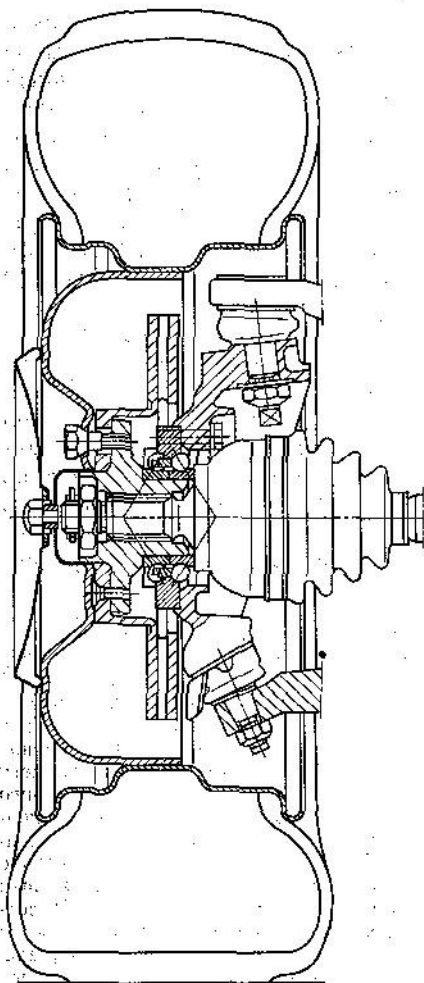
Передняя подвеска автомобиля «Ситроен CX». Наружное кольцо подшипника второго поколения прикреплено болтами к опоре подшипника колеса. Хорошо видны вентилируемый тормозной диск, надетый снаружи на фланец ступицы, и стопорение шестигранной гайки для фиксации вала колеса в ступице. Эту задачу выполняет насадное шплинтующее тонкостенное кольцо
